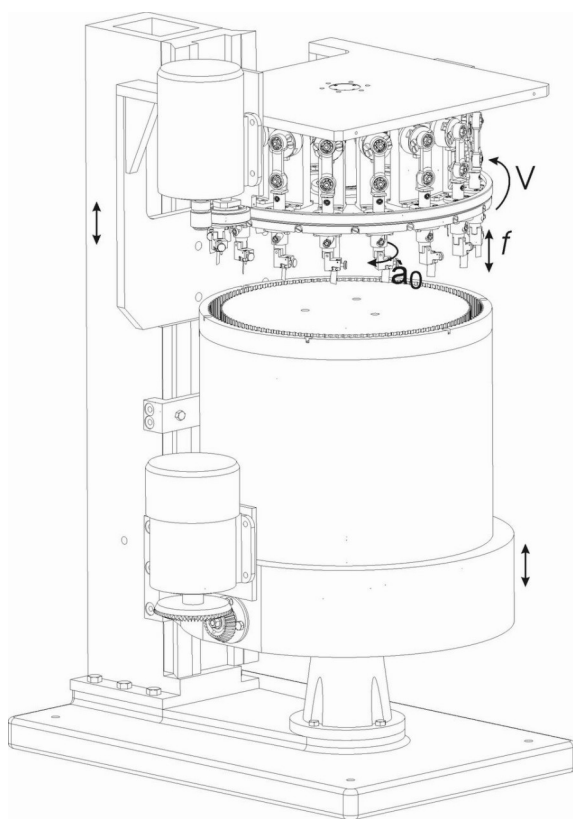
Общий вид установки для магнитно-абразивного полирования компрессорных лопаток ГТД
